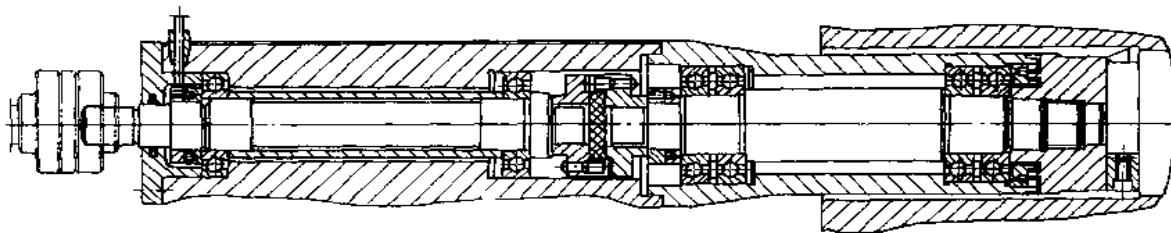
刀具钢套可进入加工件的镗削主轴结构
